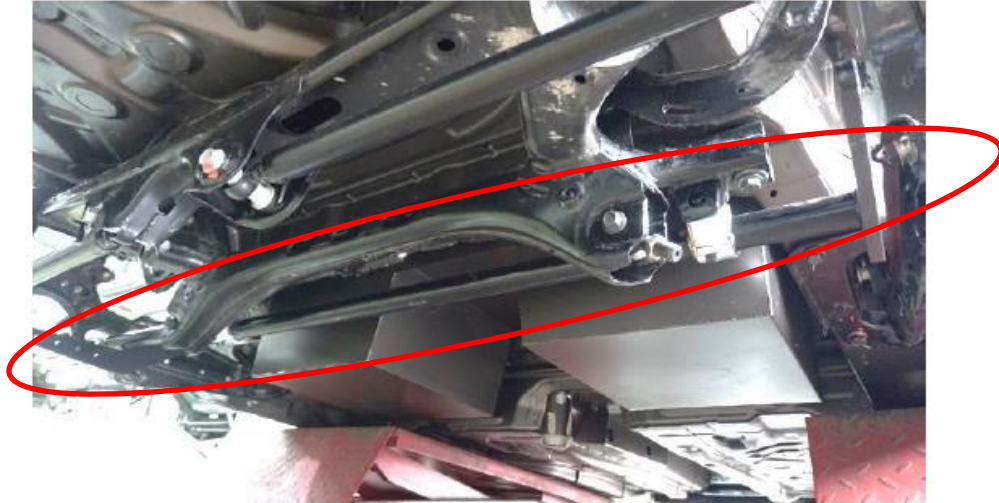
Imagen detalle de la colocación de la barra de torsión delantera. Fuente: Imagen propia.
